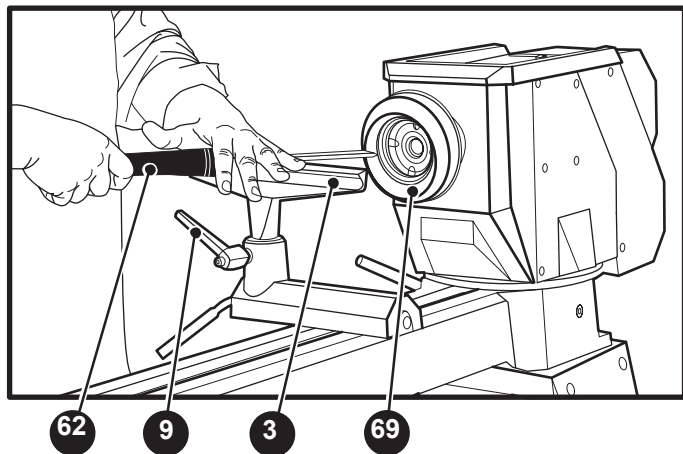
Рисунок Y — точение заготовки с повернутой на 90° передней бабкой станка.
